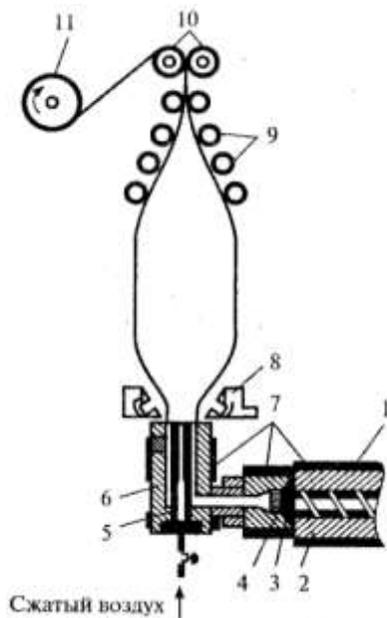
Схема изготовления пленки раздуванием трубы вверх:
